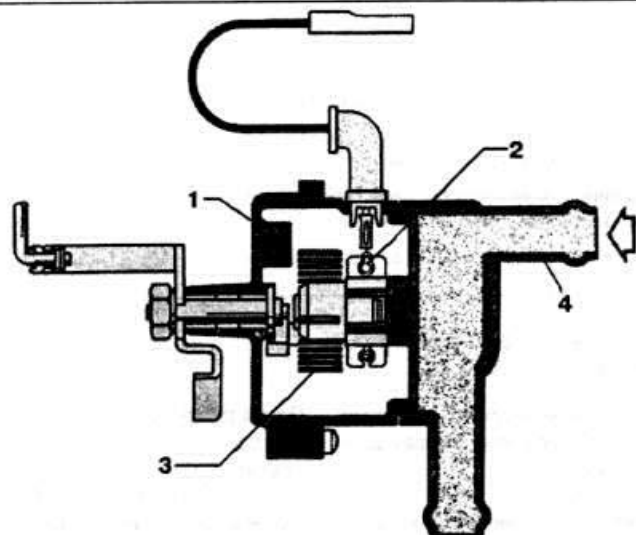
Разрез корпуса автоматического пускового устройства:
